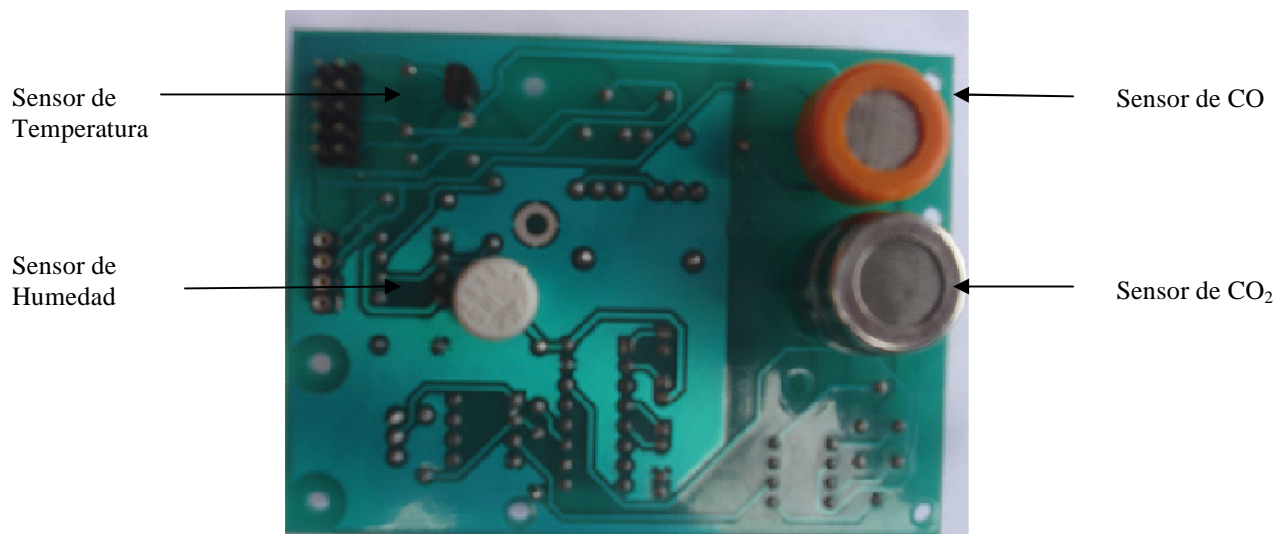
Elementos soldados en la Placa No.2
